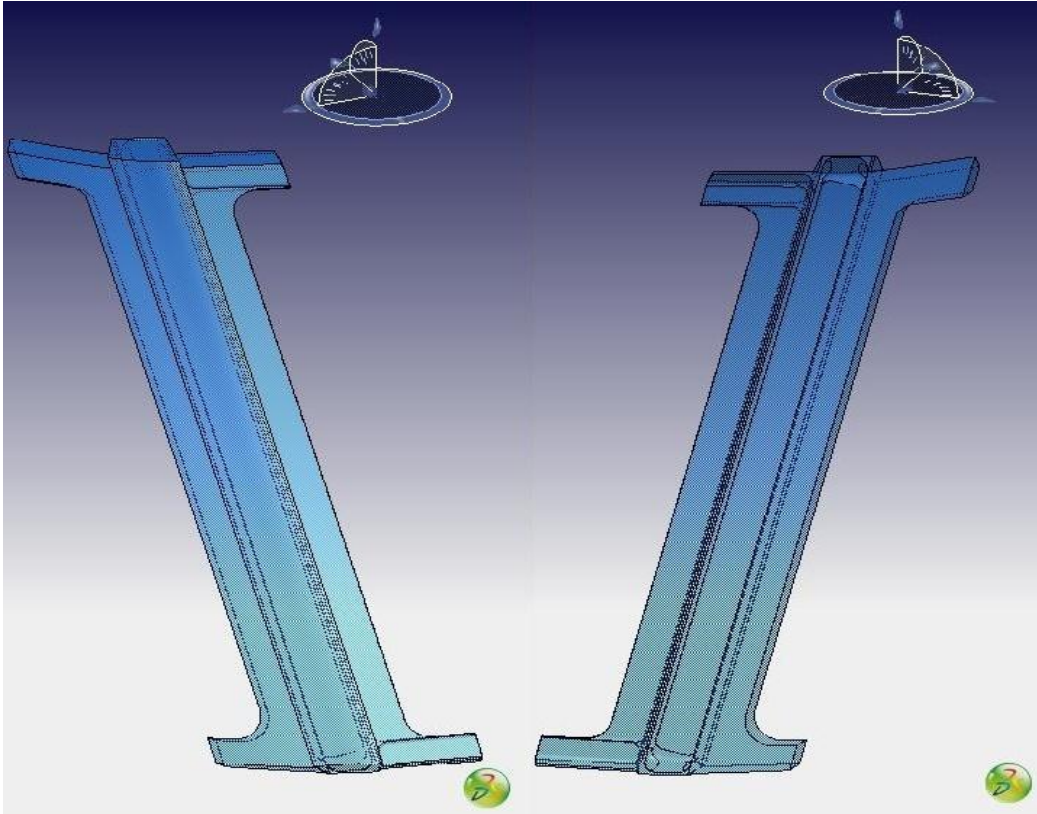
Proposta de alteração da viga lateral da estrutura.
